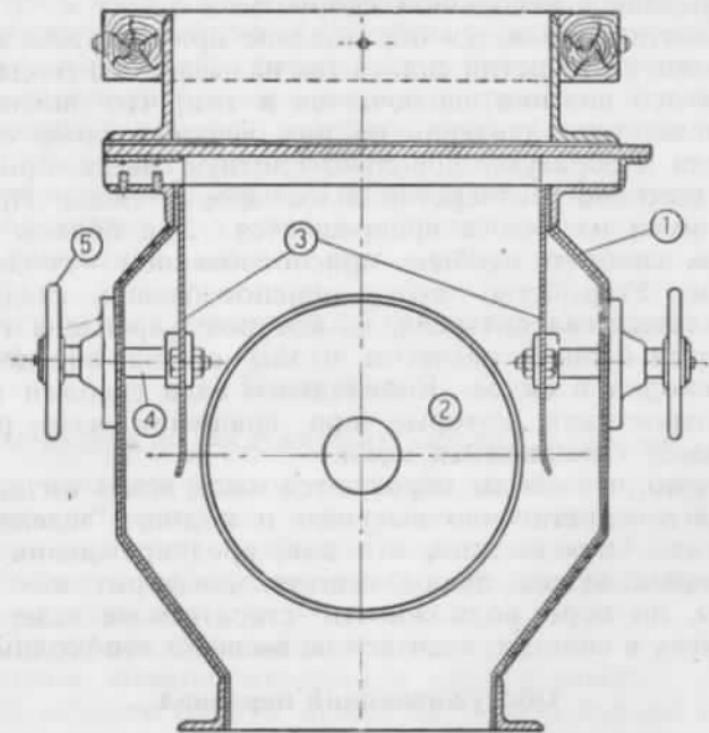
Барабанный разгружатель силосов (поперечный разрез).
